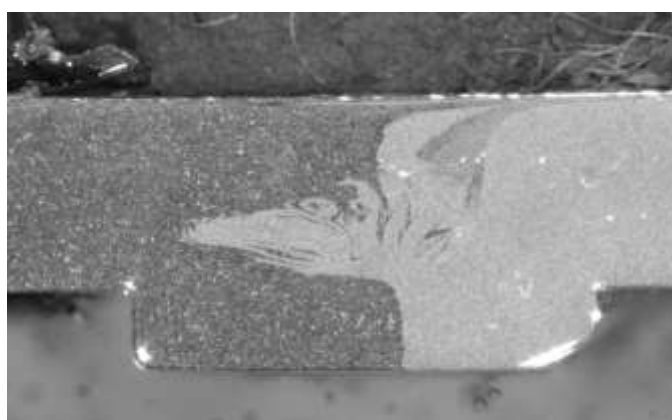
Структура сварного соединения сплавов В-1579 и АМг6
